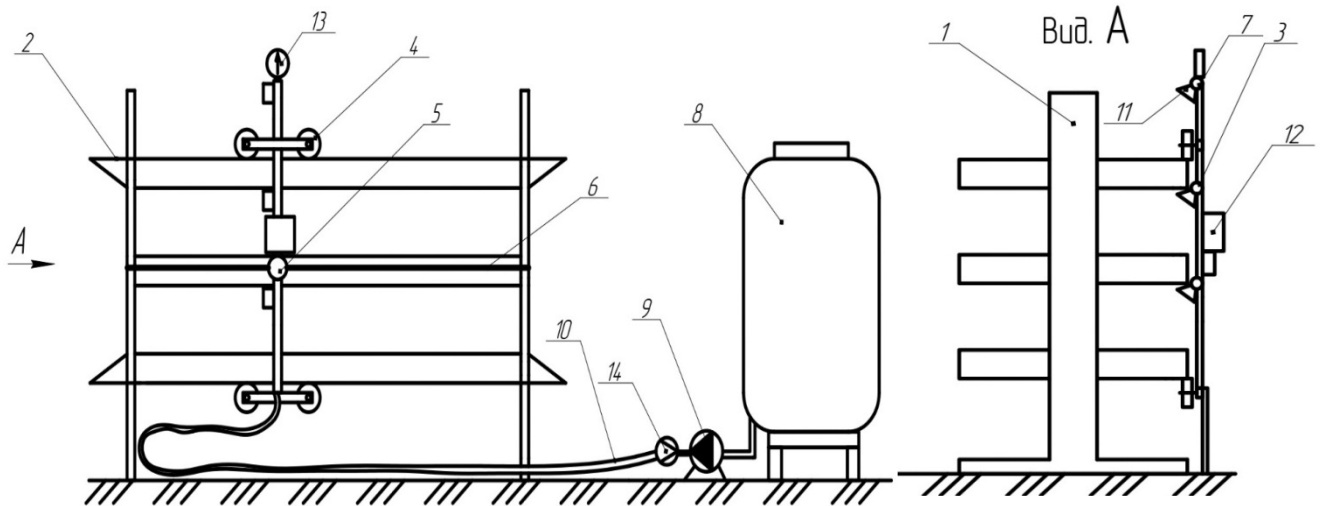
Схема поливной установки: 1 – сварная конструкция стеллажного типа; 2 – металлические рельсовые направляющие; 3 – боковая каретка; 4 – роликовые опоры; 5 – шаговый двигатель; 6 – канат; 7 – гидравлические клапаны с электромагнитным клапаном; 8 – резервуар; 9 – гидравлический насос; 10 – гибкий трубопровод; 11 – дождевальная насадка; 12 – блок управления; 13, 14 – соответственно датчики давления и расхода воды
